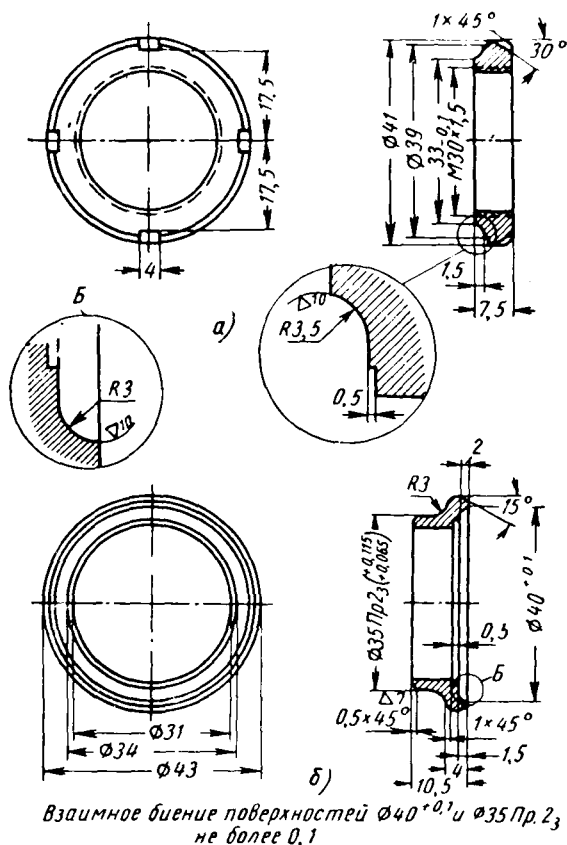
Детали верхнего подшипника поворотной трубы передней подвески мотороллеров ВП-150 и В-150М:
